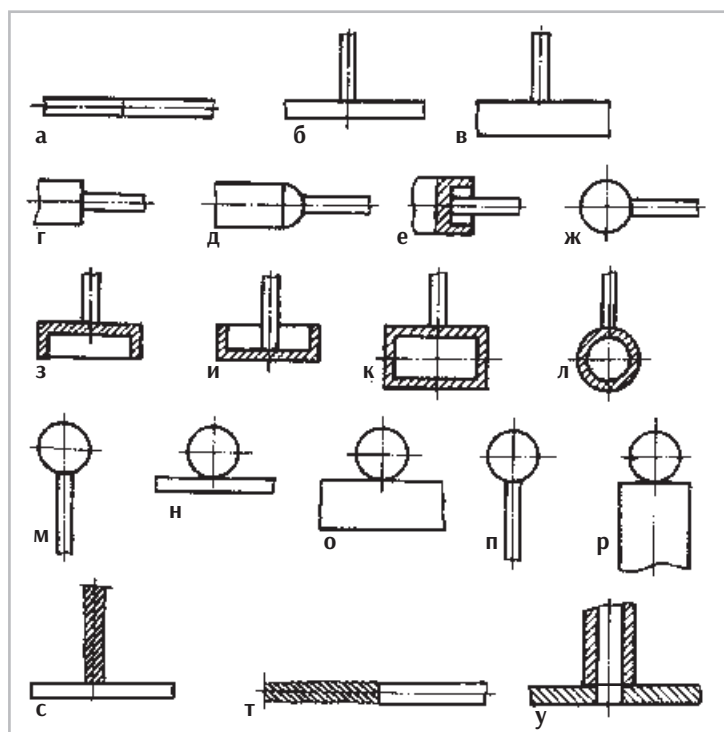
Эскизы сварных соединений, выполняемых различными способами дугоконтактной сварки
